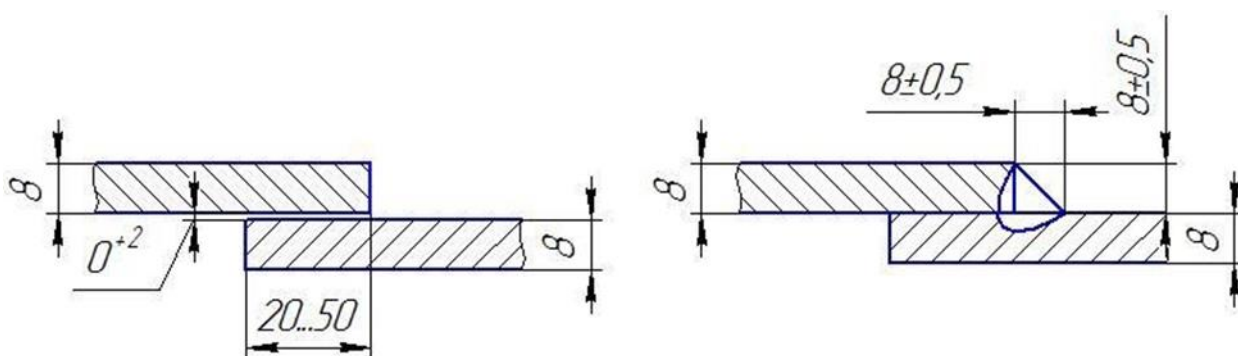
Сварной шов приварки окрайки к центральной части дна
